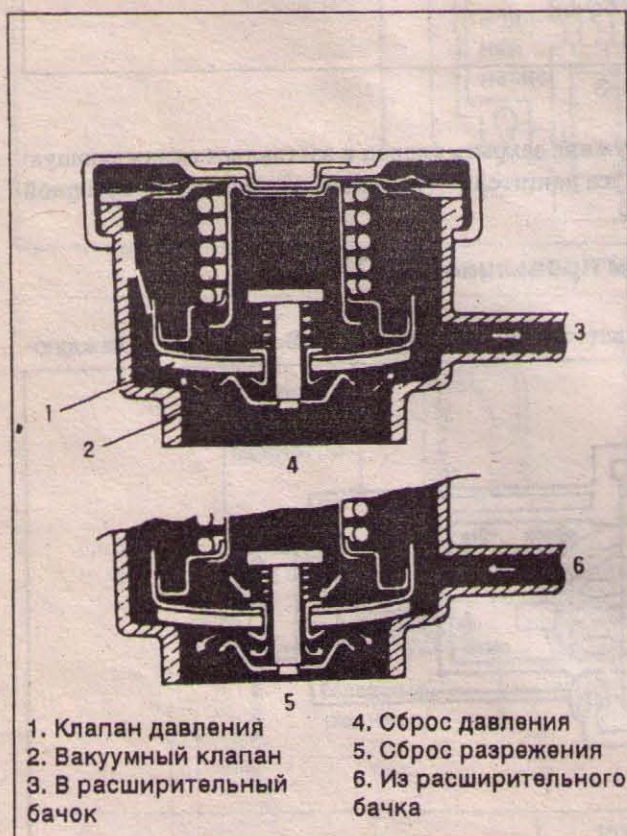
В—5 РАДИАТОРНАЯ КРЫШКА ВПУСКА И ВЫПУСКА ДАВЛЕНИЯ
